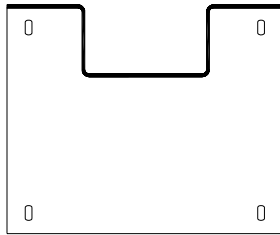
Installation de la trousse de retenue de façade / Installation of the rock retainer kit
